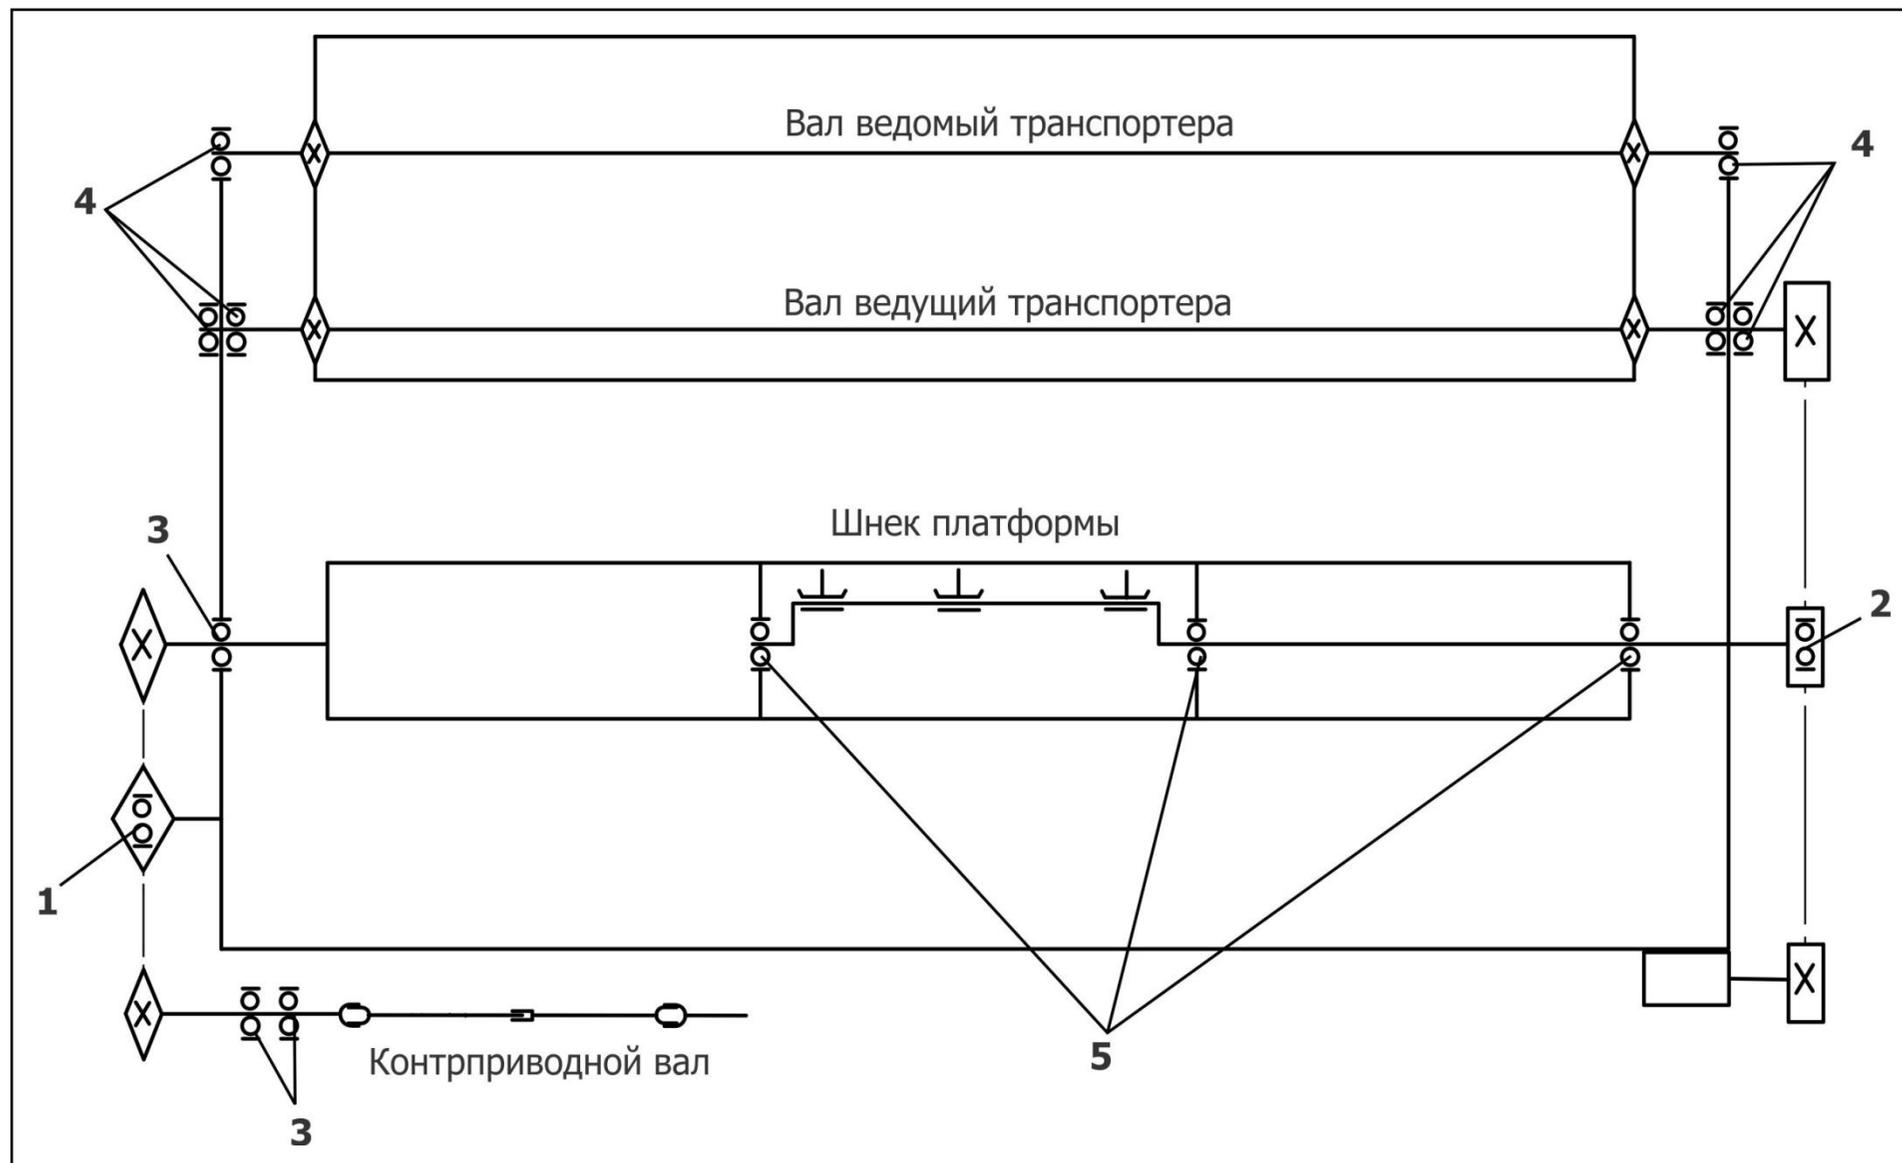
Схема расположения подшипников платформы-подборщика
